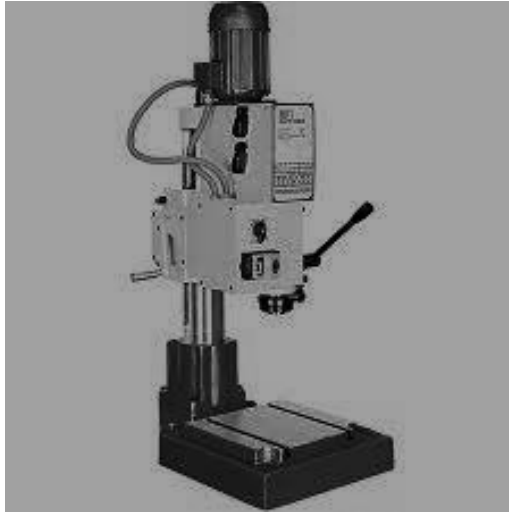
Свердлильно-вертикальний верстат KST16V
